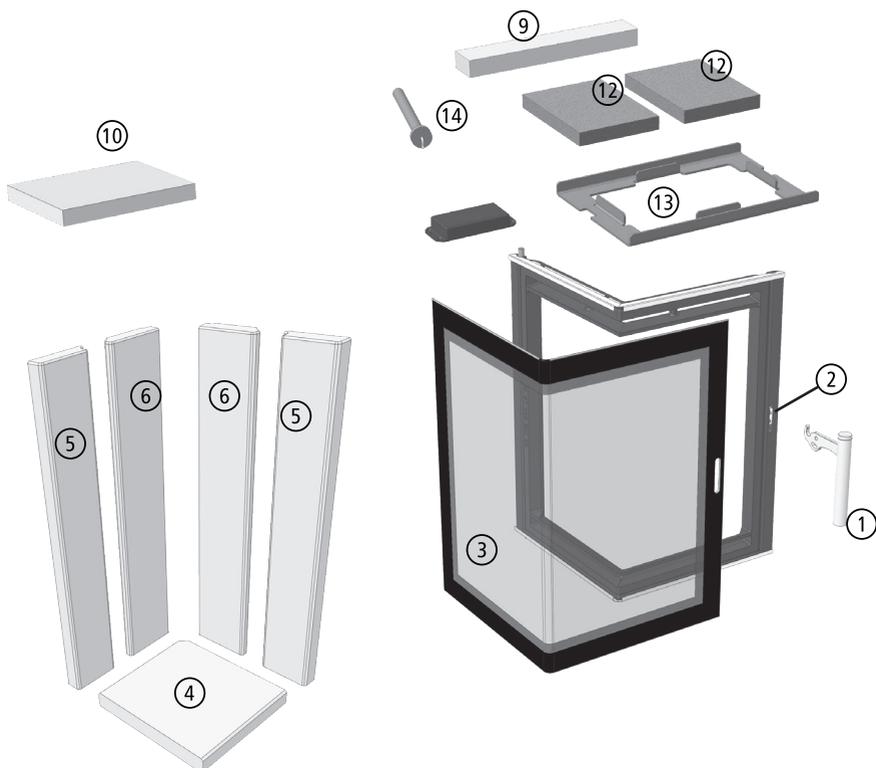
Aperçu des pièces de rechange pour CORNA tec
